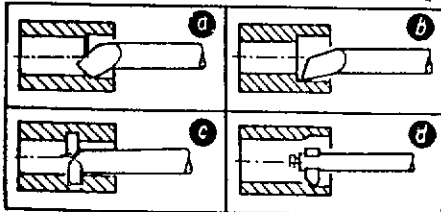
Útiles de cilindrar interiormente. a) Util para desbastar interiormente; b) útil de corte lateral para tornado interior; c) útil de gancho; d) barra o eje de taladrar provisto de cuchilla postiza.
